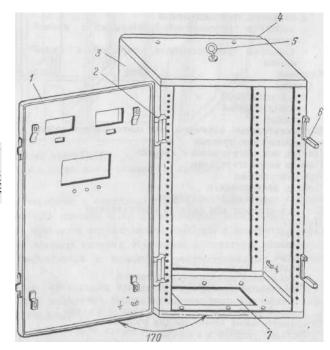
Щит шкафной малогабаритный: /— дверь; 2— петля; 3— каркас; 4— панель; 5— рым-болт; 6— замок; 7— крышка
